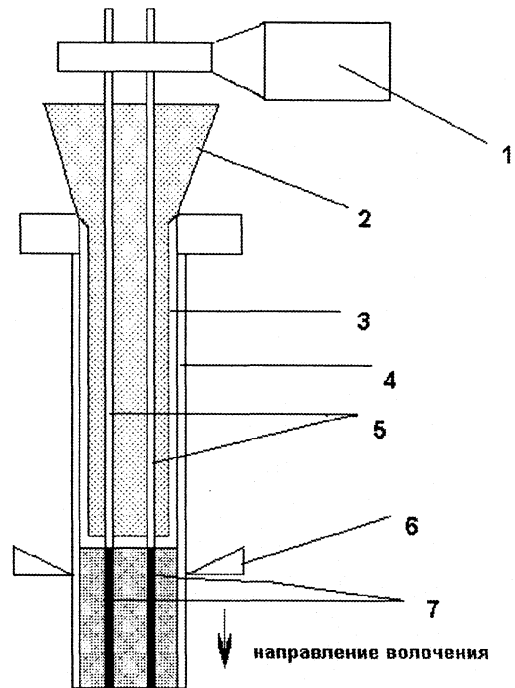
Схема засыпки порошковой изоляцией кабельной заготовки с использованием ультразвуковых колебаний: 1 – магнитострикционный преобразователь-концентратор; 2 – бункер; 3 – направляющая труба (шток); 4 – труба-заготовка; 5 – направляющие трубки для жил; 6 – вибратор; 7 – токопроводящие жилы
